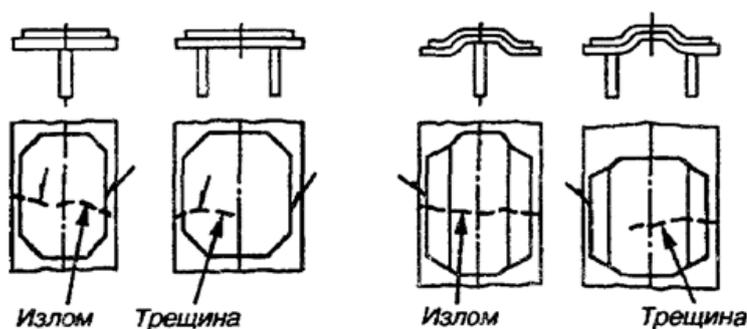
Верхние листы промежуточных и шкворневых балок, отремонтированные сваркой.
